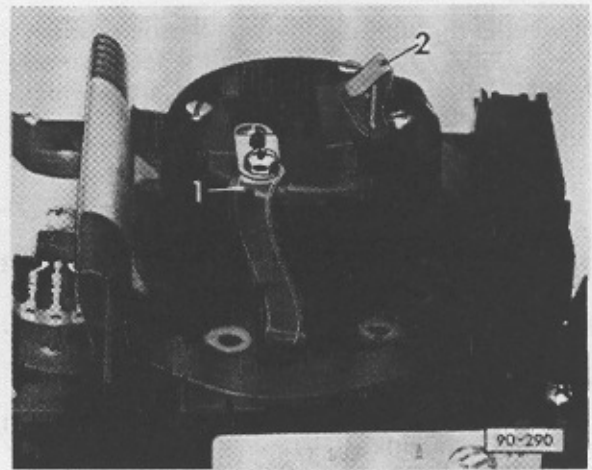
Befestigung für Anschlüsse Zeituhr
